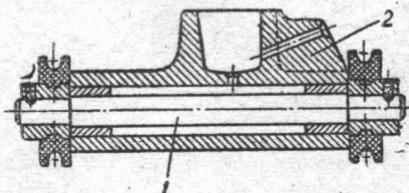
Промежуточный вал наматывателя в разрезе: 1 — промежуточный вал; 2 — подшипник
